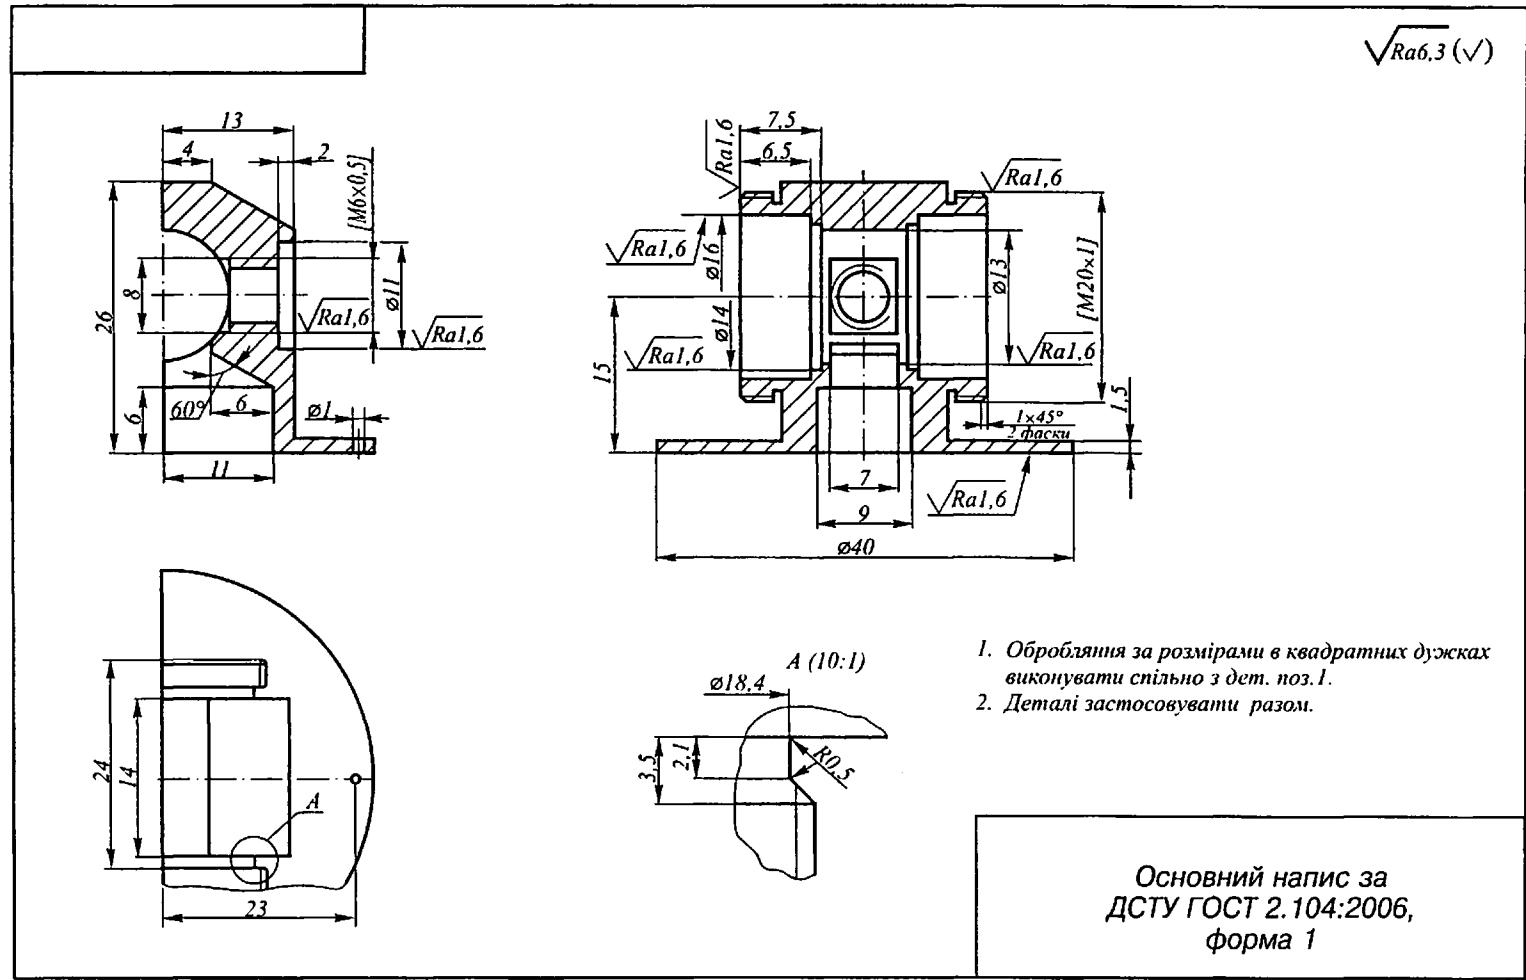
Приклад оформлення кресленника корпусної деталі
